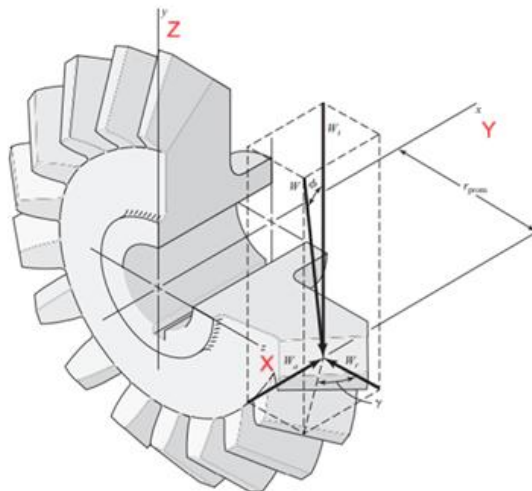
Componentes de la fuerza resultante en u engranaje cónico[41]
